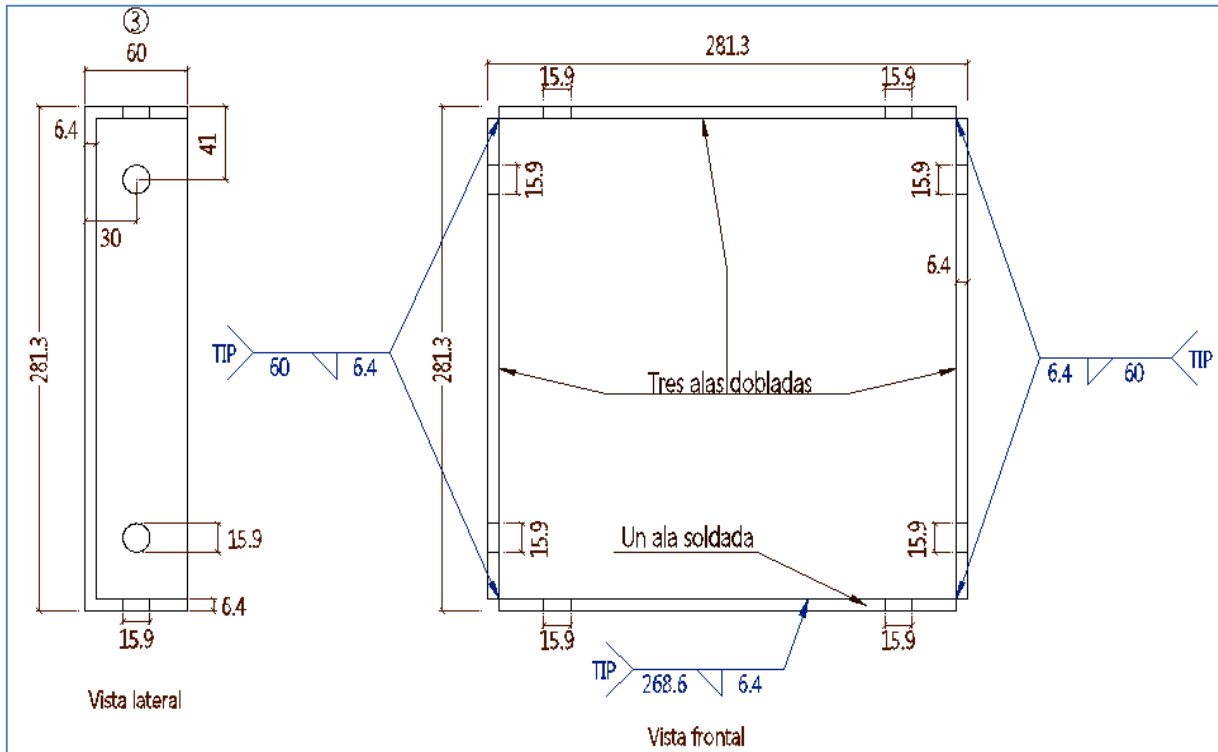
Detalle despiece pieza No.3 modelo 3 tensión.
